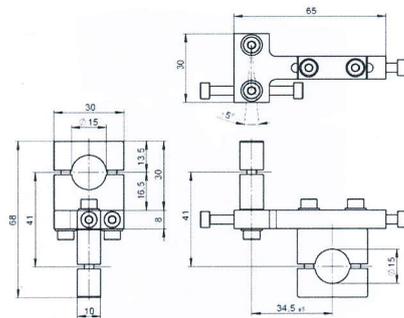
Support B3-LD, plan coté (mesures en mm)
